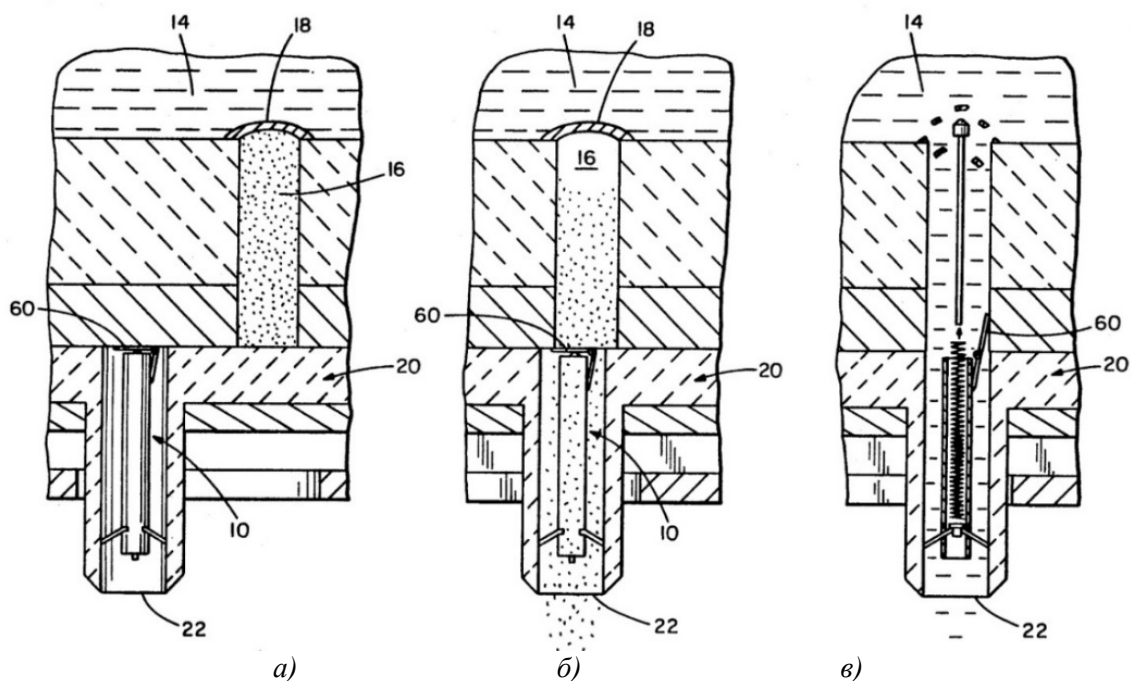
Устройство для разрушения твердой корки на входе в сталевыпускной канал разливочного ковша: а) при закрытом затворе; б) в процессе сдвига шибберных плит; в) при открытии ковшового затвора
